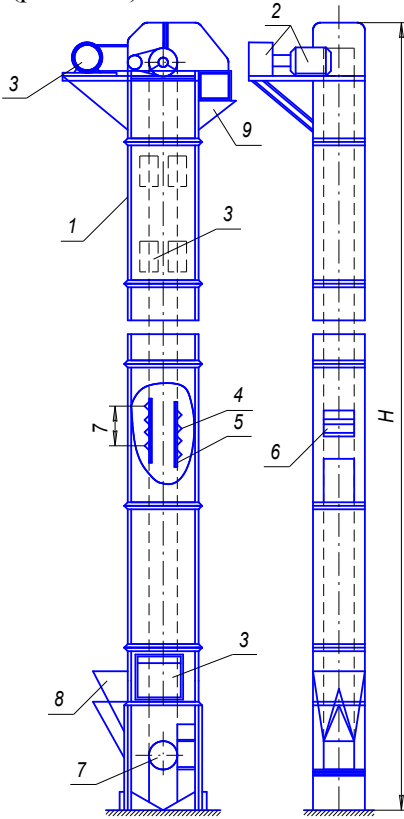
Элеватор ковшовый ленточный типа ЭЛ:
